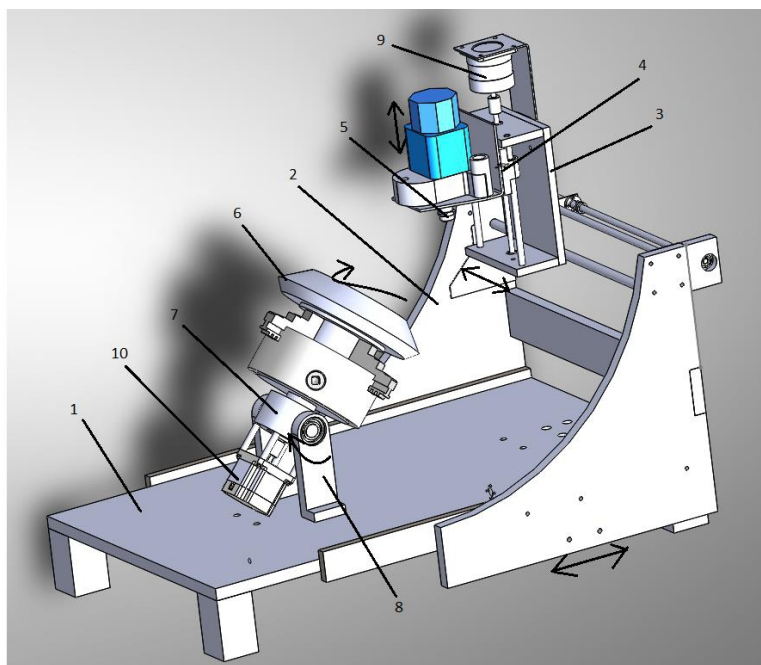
Компоновка станка с ЧПУ для обработки зубьев конических зубчатых колес
